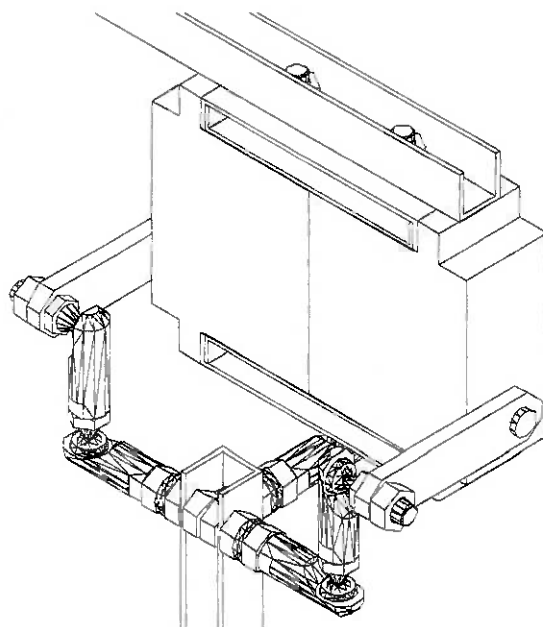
Desenho de conjunto do joelho – vista isométrica
